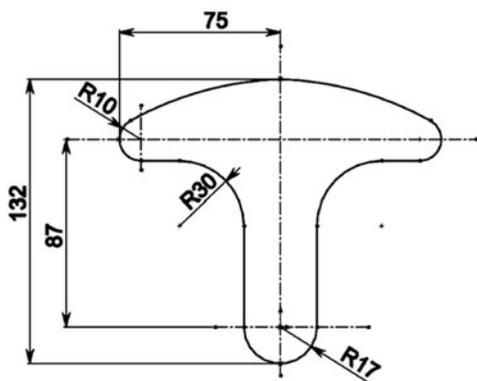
Эскиз заготовки изделия “Поводок”
